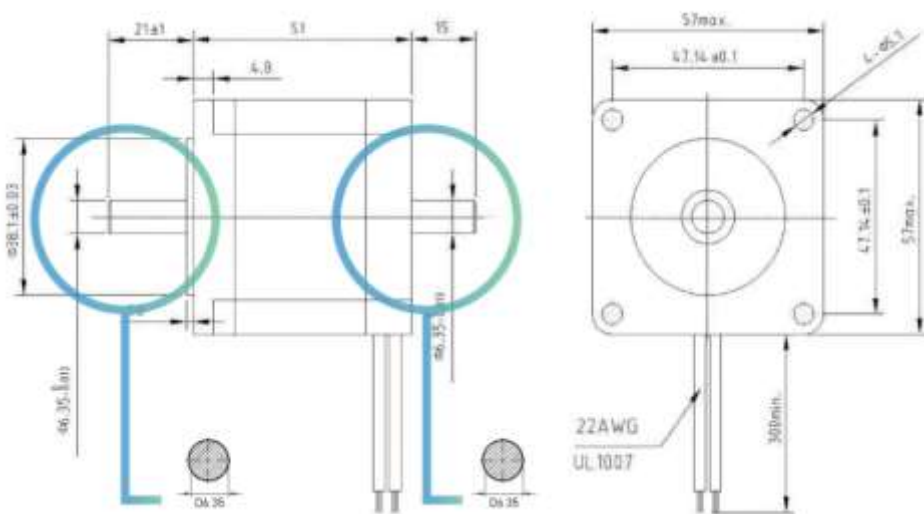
Габаритне креслення крокового двигуна NEMA23 57HS5128B4
